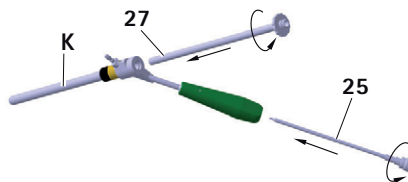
Montaggio bussola guida Ø 3,5 mm/4,0 mm
